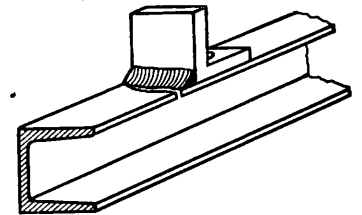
Bruch an einem Längsträger mit aufgeschweißtem Eckwinkel.
